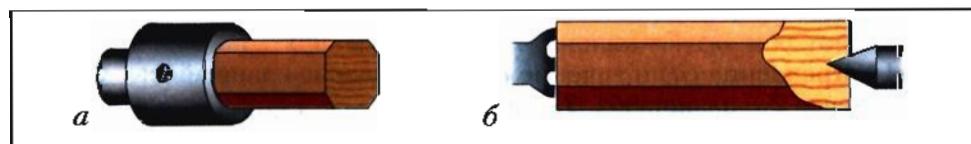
Крепление детали: *а* – в патроне винтом, *б* – трезубцем с поджатием конусом задней бабки
